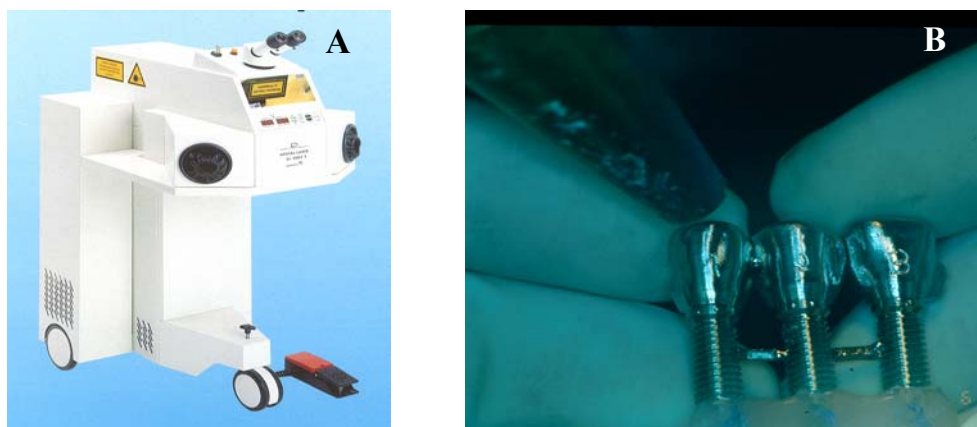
A - Aparelho de soldagem a laser. B – Vista do conjunto sendo soldado dentro da câmara
